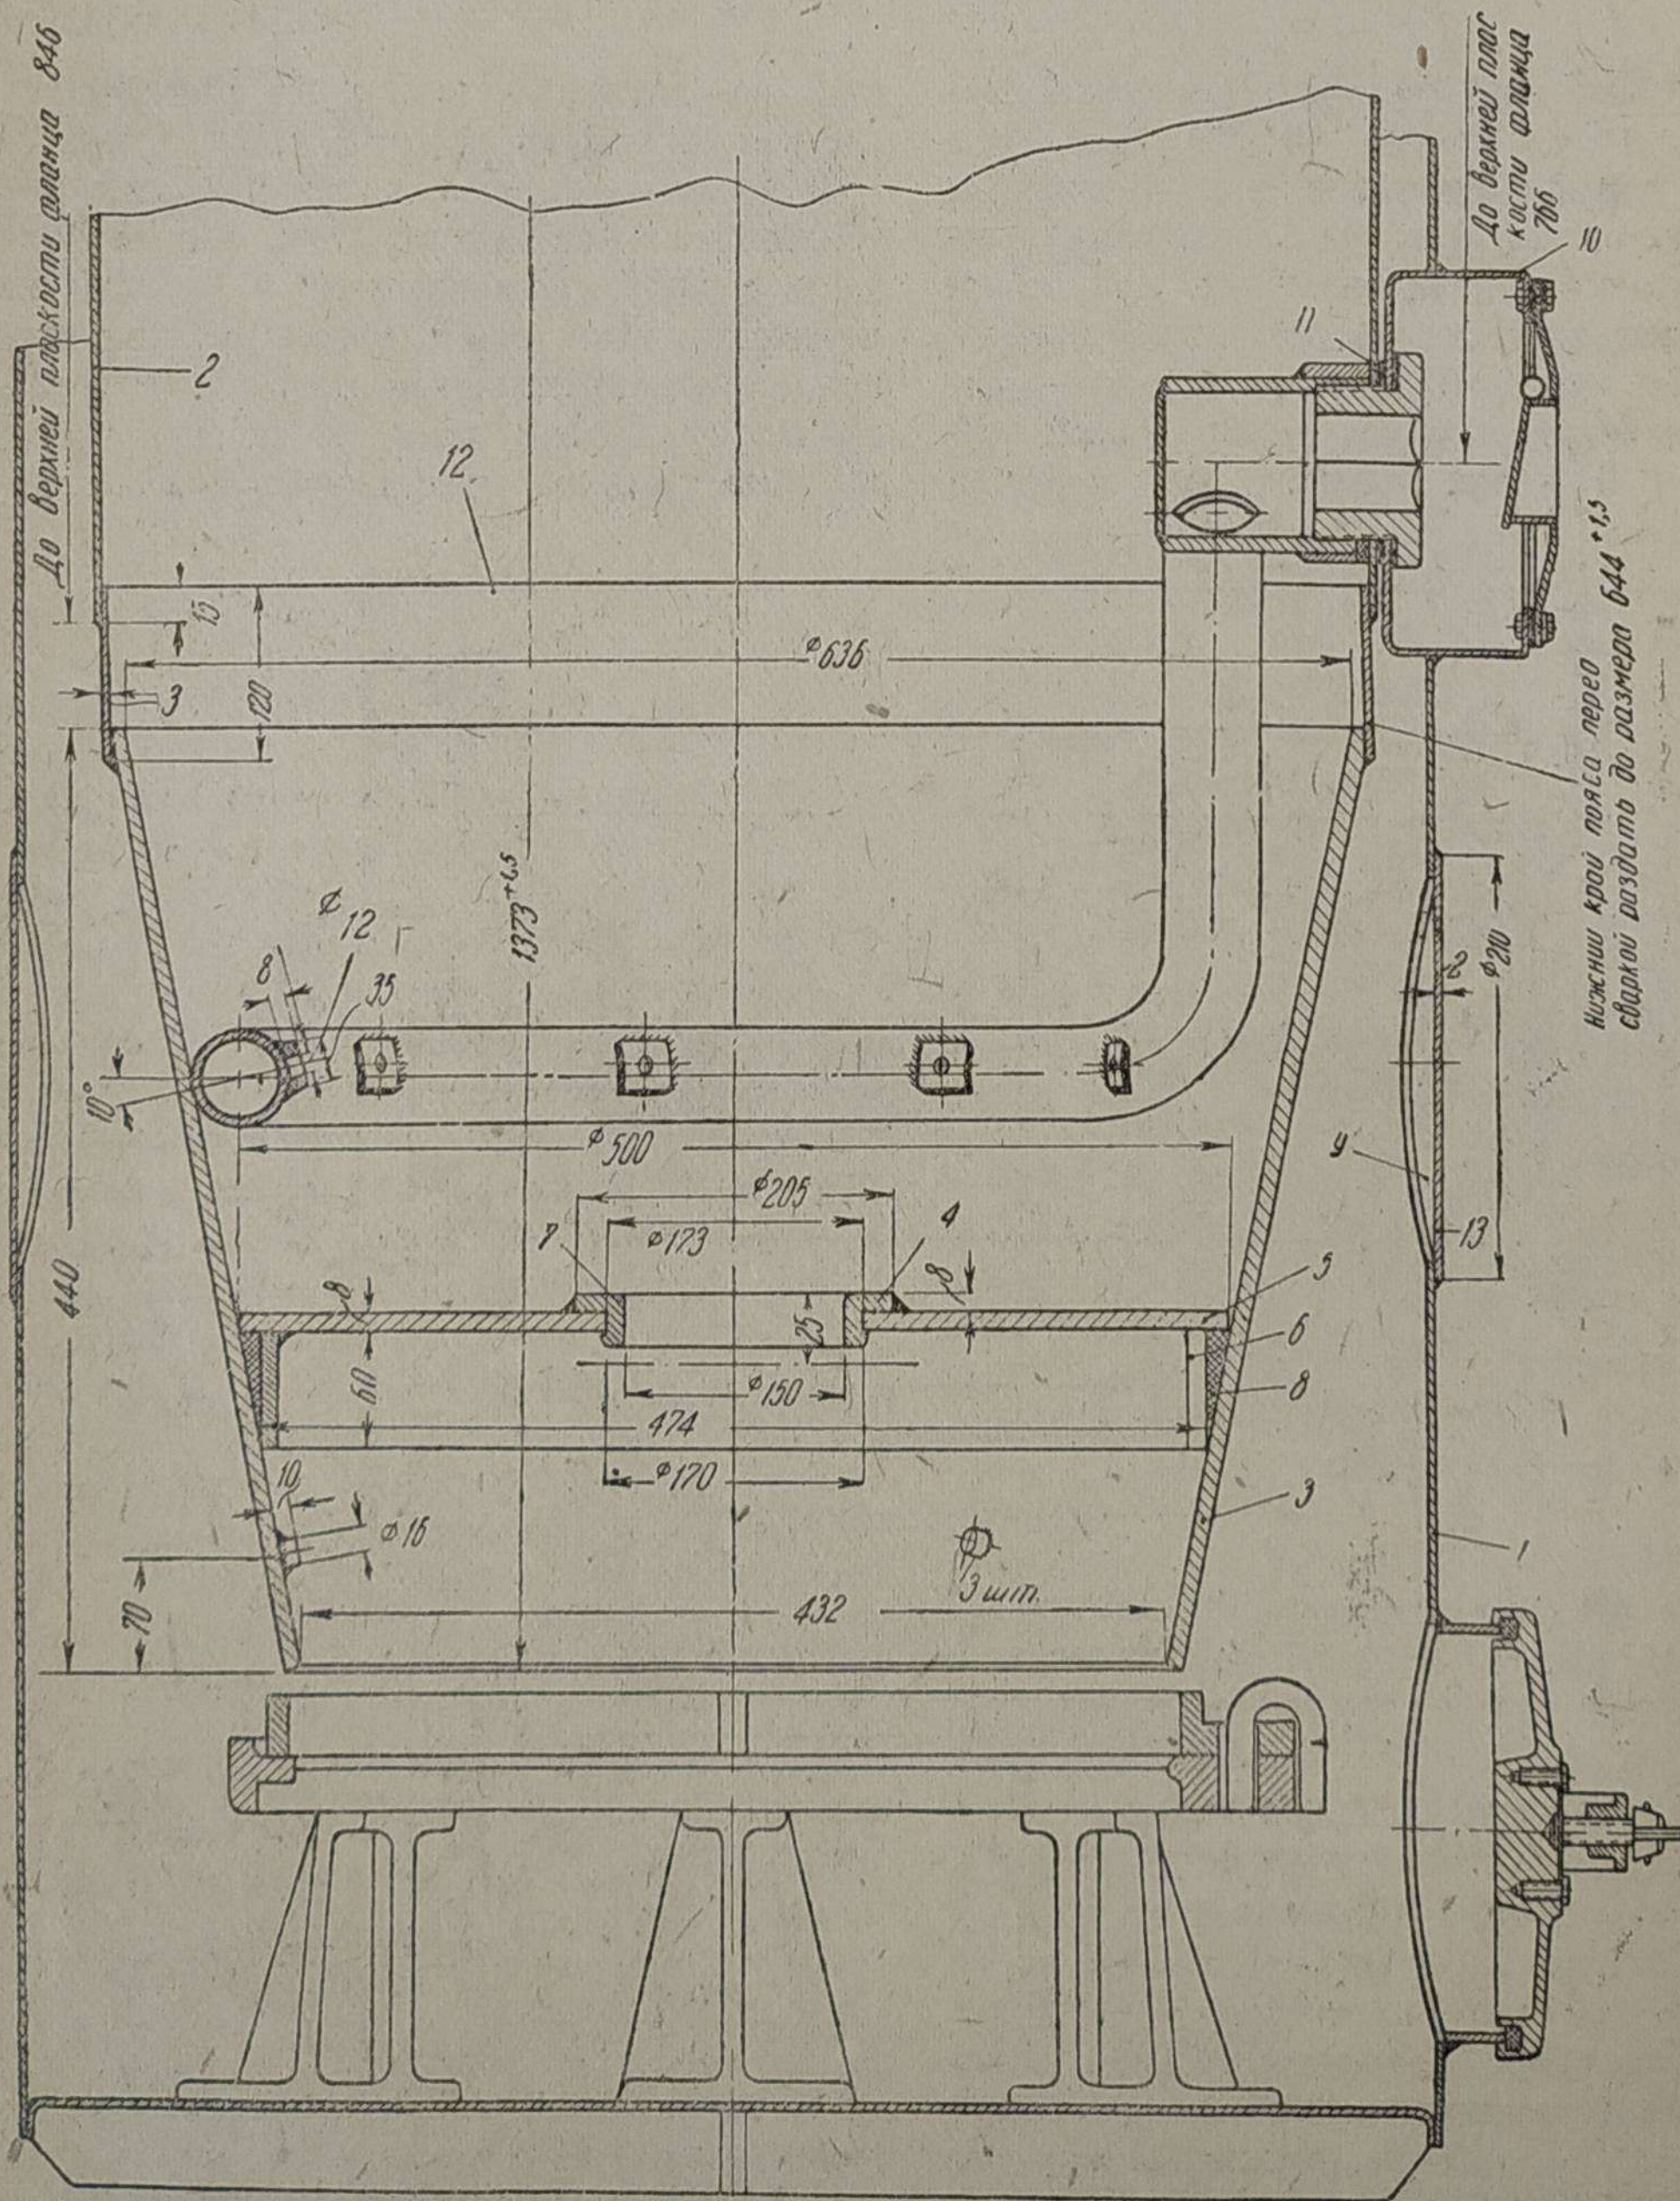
Общий вид газогенератора с заменённым топливником для трактора «УТЗ-СГ-65». 1 — корпус газогенератора, 2 — цилиндр бункера, 3 — конус топливника, 4 — диск в сборе, 5 — диск, 6 — обечайка диска, 7 — горюшина диска, 8 — асбестовый шнур, 9 — накладка отверстия воздушной коробки, 10 — воздушная коробка в сборе, 11 — прокладка футорки в сборе, 12 — пояс бункера газогенератора, 13 — отверстие пробки.
